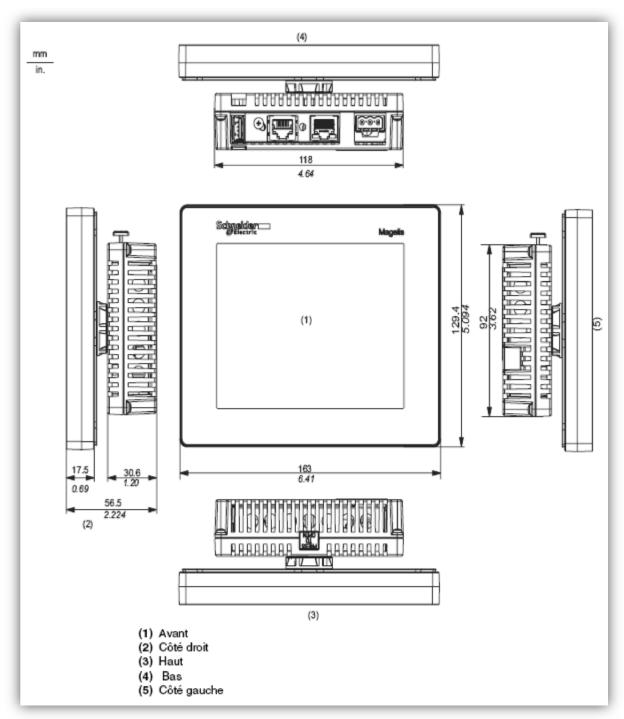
Dimensions de l'ensemble de l'écran tactile
